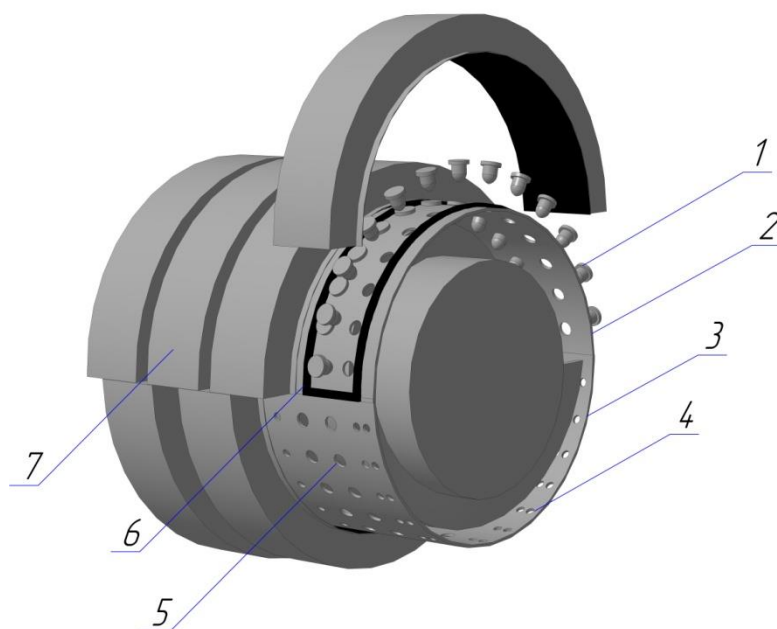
Конструкция активной деки домолачивающий аппарат, патент на полезную модель № 86546: 1 – шипы; 2 – верхняя дека; 3 – нижняя дека; 4 – отверстия для вывода зерна; 5 – отверстия под шипы; 6 – резиновая прокладка; 7 – пневмоподушка.
